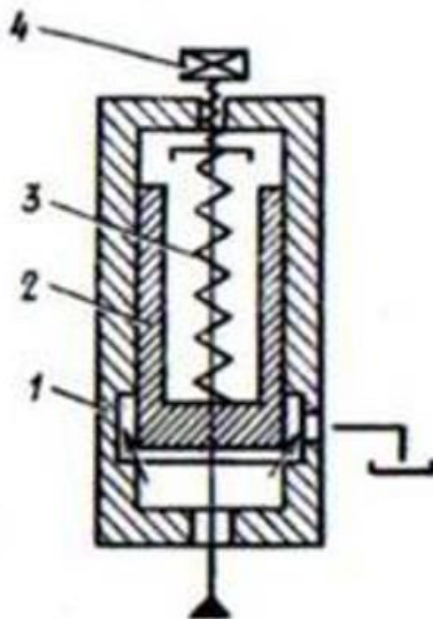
Схема переливного клапана прямого действия: 1 - корпус; 2 - золотник; 3 - пружина; 4 - регулировочный винт.
